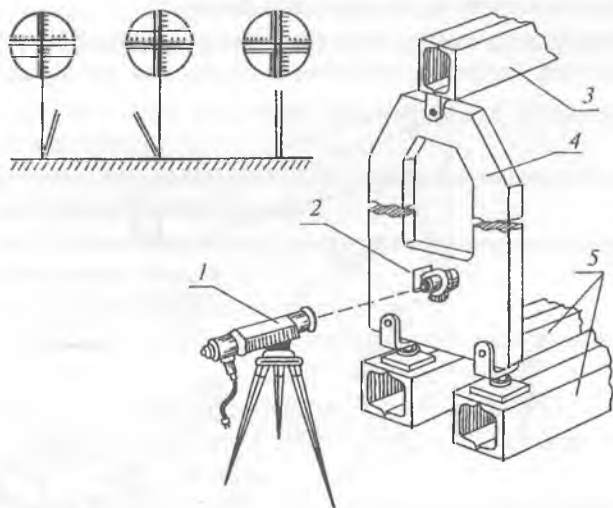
Схема установки (и проверки) автоколлиматором вертикальности плиты сборочного приспособления: 1 — автоколлиматор; 2 — отражающее зеркало; 3 — верхняя балка приспособления; 4 — плита фиксации разъема собираемого агрегата; 5 — нижние балки приспособления
